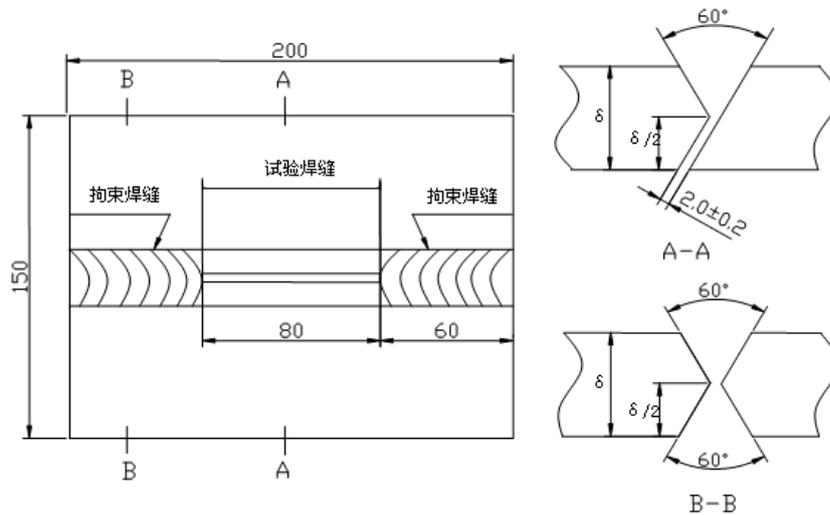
斜 Y 坡口焊接裂纹试件的形状和尺寸
